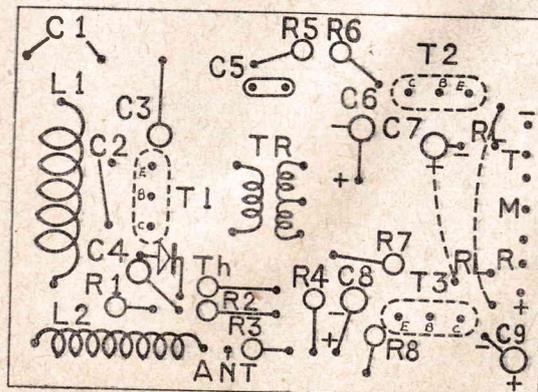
La plaquette à câblage imprimé pour le montage du récepteur
